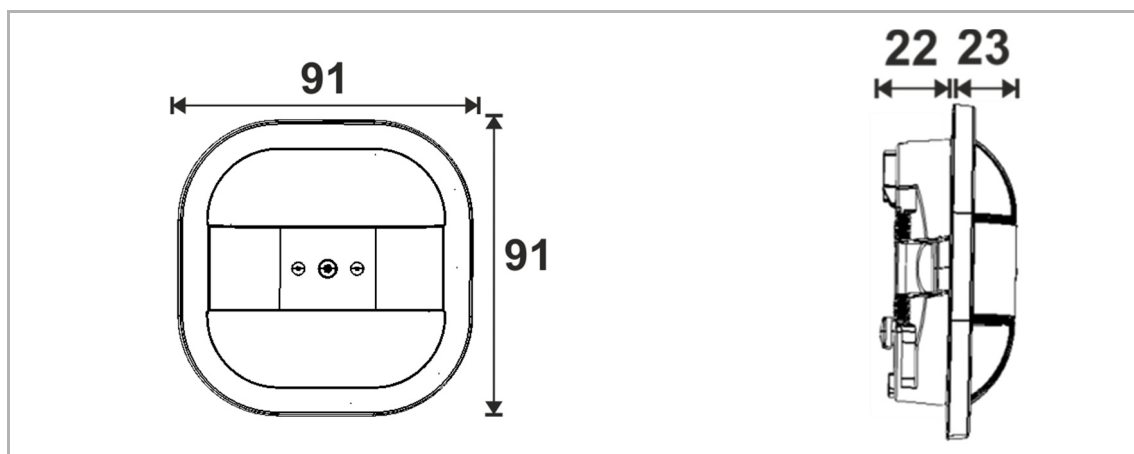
Dimensions du Busch-Guard Sky KNX
